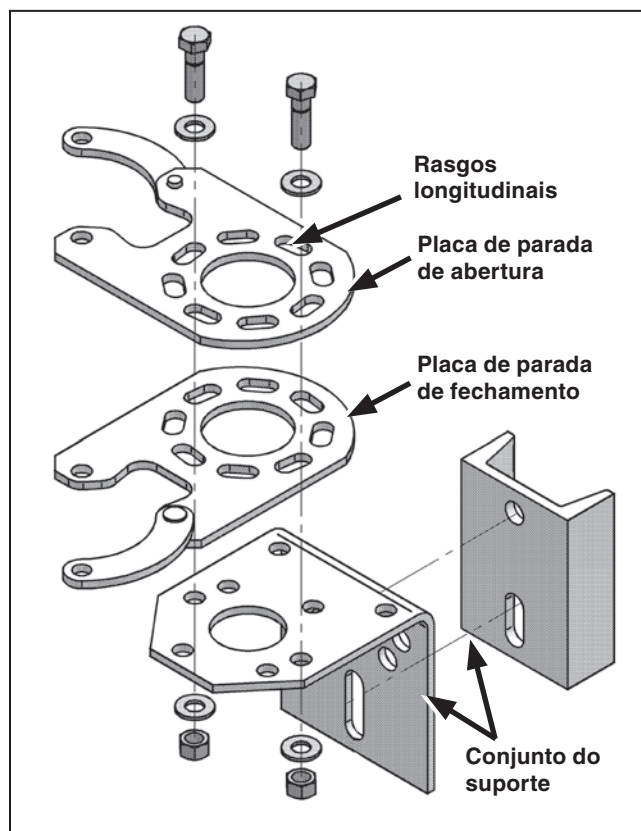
Placas de parada e conjunto da sapata-base—vista explodida.
